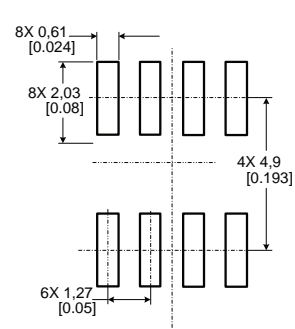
SOIC-8 SMD安装尺寸、PCB焊盘布局和引脚 (仅供参考: mm/[英寸])
